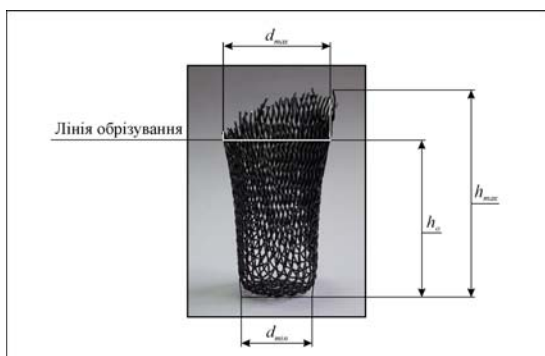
Третє витягування циліндричної деталі із металевої сітки
